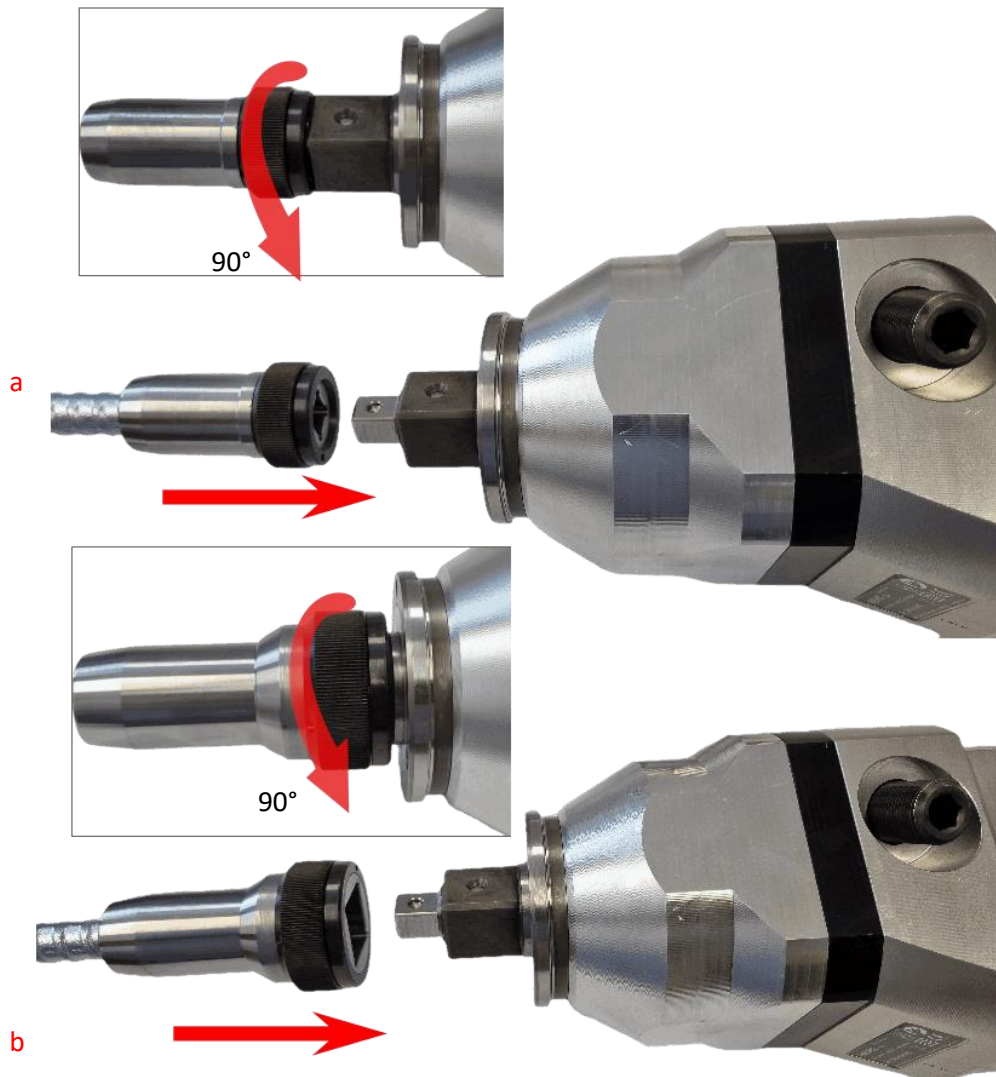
Werkzeugeinsatz auf der Ein-/Ausdrehmaschine
